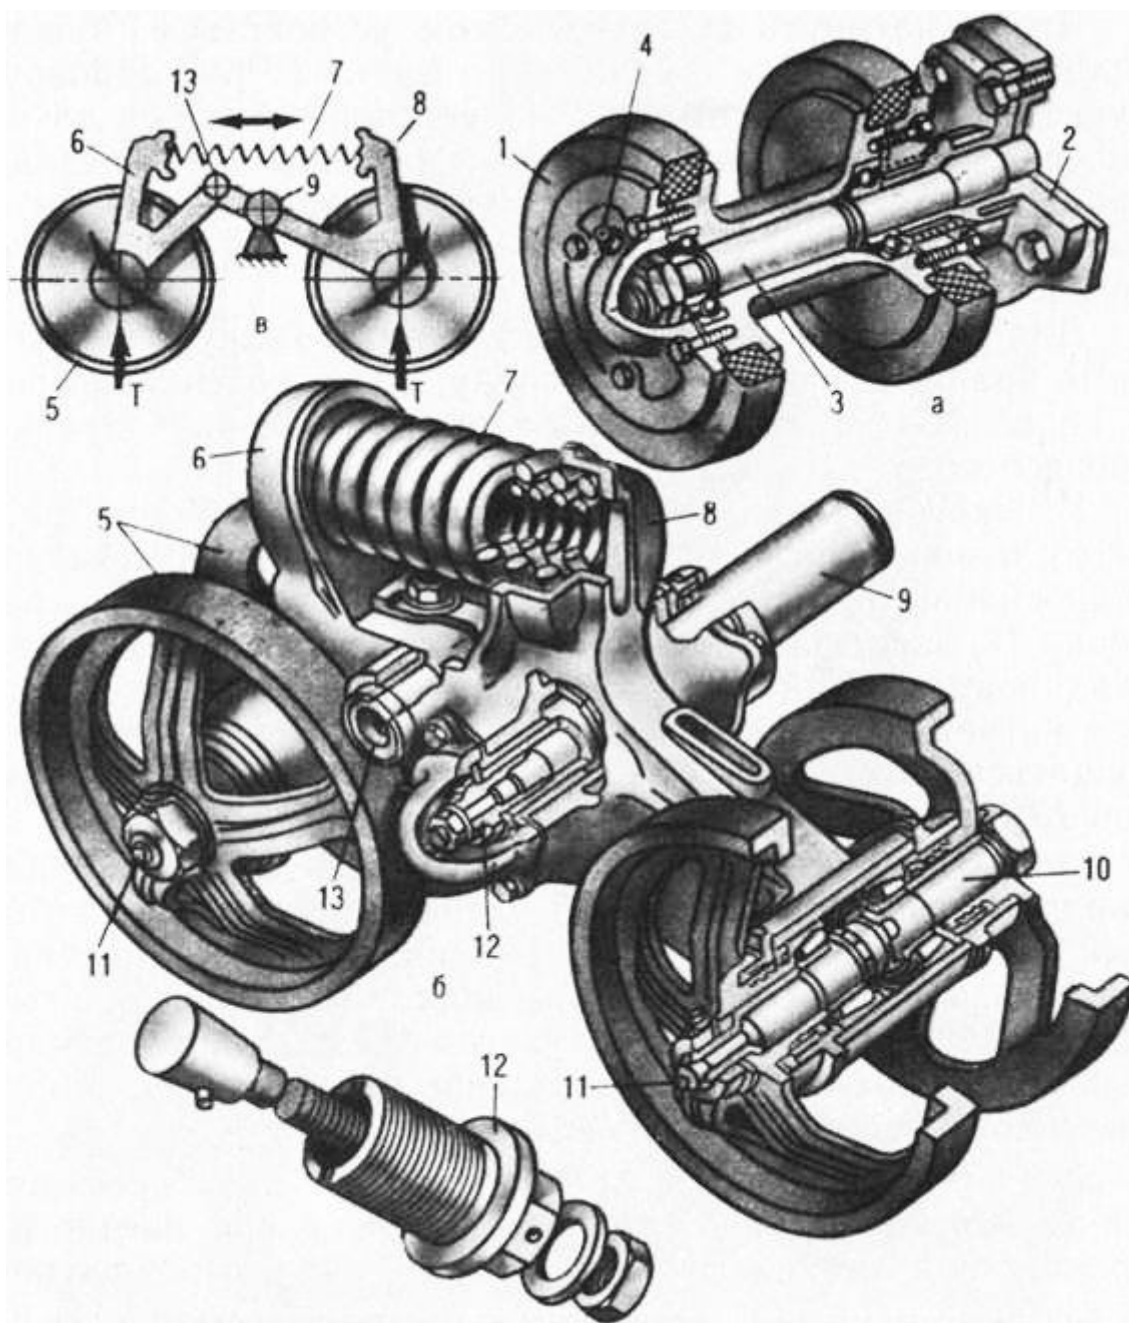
Частини гусеничного рушія [1]: а-підтримуючий ролик; б - каретка; в - схема дії каретки; 1-бандаж; 2 - кронштейн; 3, 10, 13 - осі; 4, 11 - пробки; 5 - опорні ковзанки; 6,8 - балансири; 7 - пружини; 9 - цапфа; 12 - цангова гайка.
